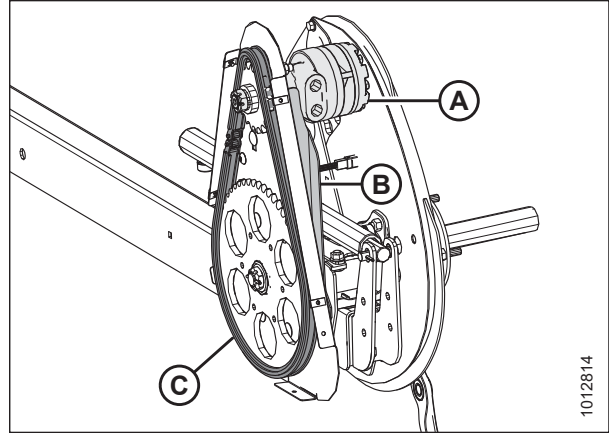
Зображено привод одинарного мотвила — привод подвійного мотвила має таку ж конструкцію
